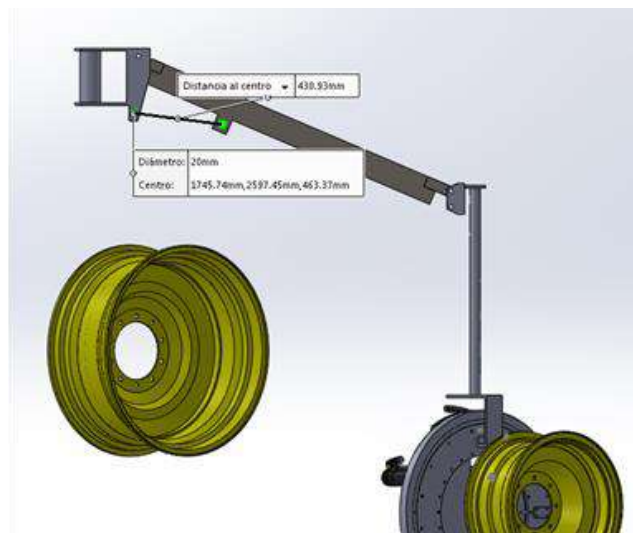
Carrera del pistón en posición inferior del brazo.
